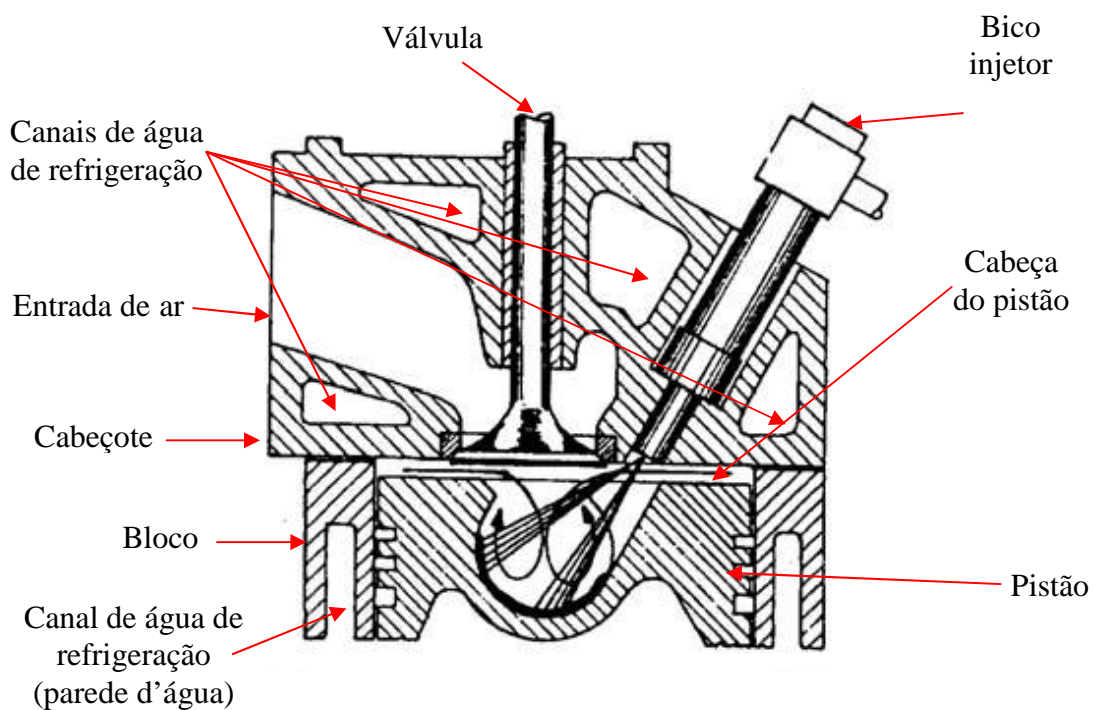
Corte da parte superior de um motor ICO refrigerado a água.
